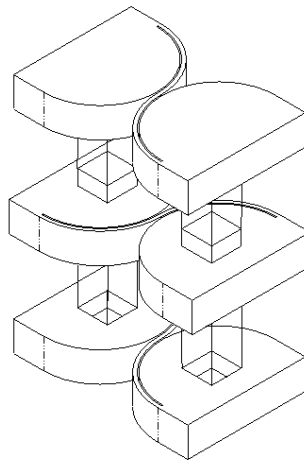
Assemblage d'un joint X_R fabriqué par électro-érosion.
